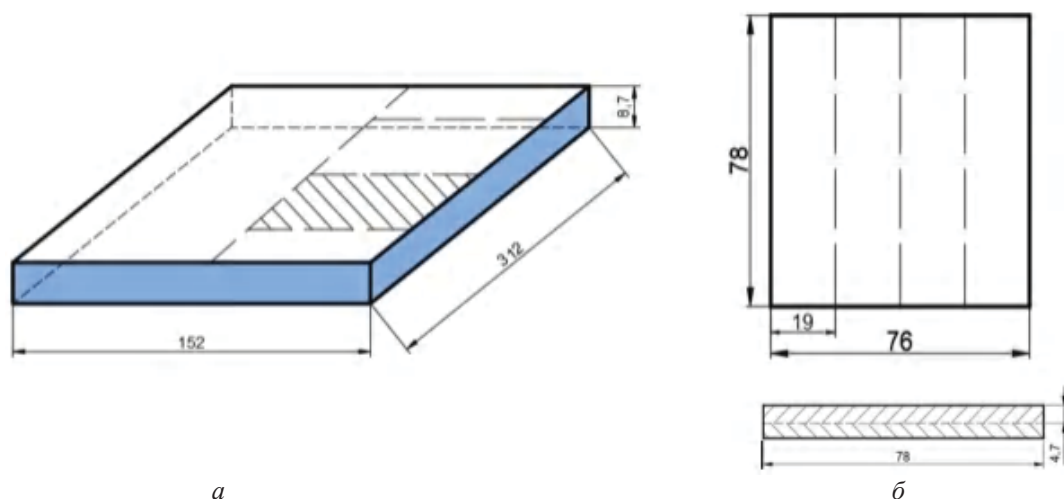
Схема вырезки образца из сваренного взрывом КМ (а) и подготовка образцов для прокатки (б)
